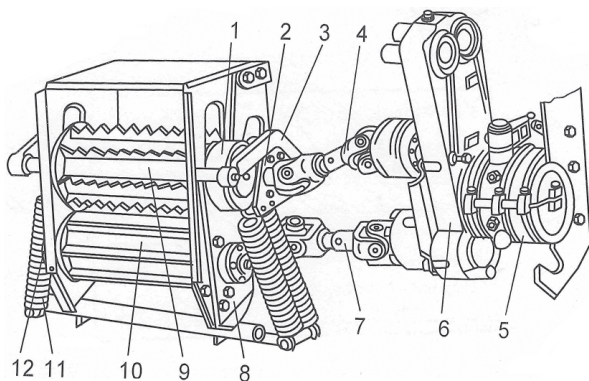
Питающий аппарат: 1 – редуктор подпрессовывающих валцов; 2 – навеска; 3 – рычаг; 4, 7 – карданные валы; 5 – коробка передач; 6 – редуктор; 8 – корпус; 9 – верхний валец; 10 – нижний валец; 11 – пружина; 12 – редуктор нижних валцов
